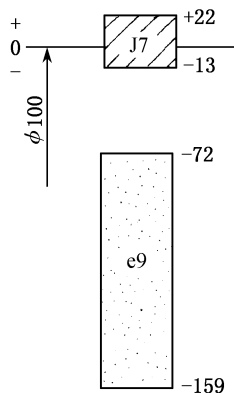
箱体孔与端盖定位圆柱面的公差带示意图
